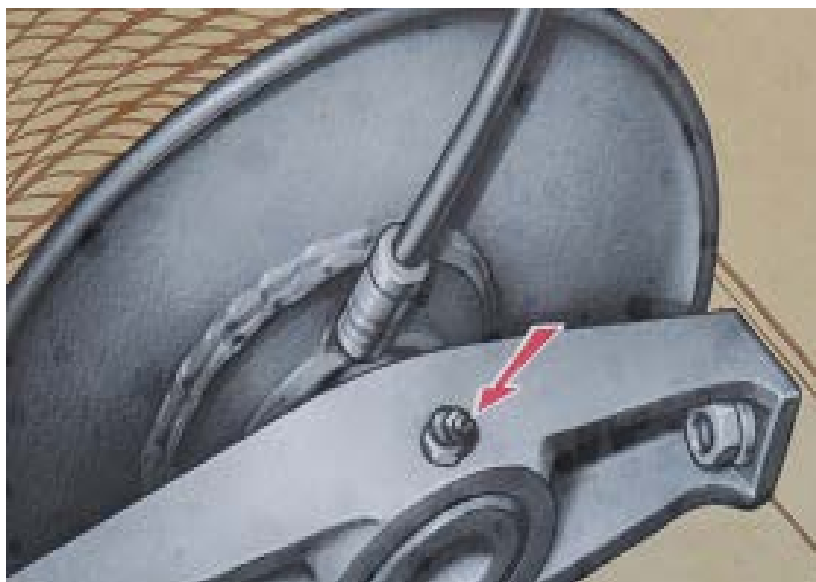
Смазка подшипников барабана лебёдки
